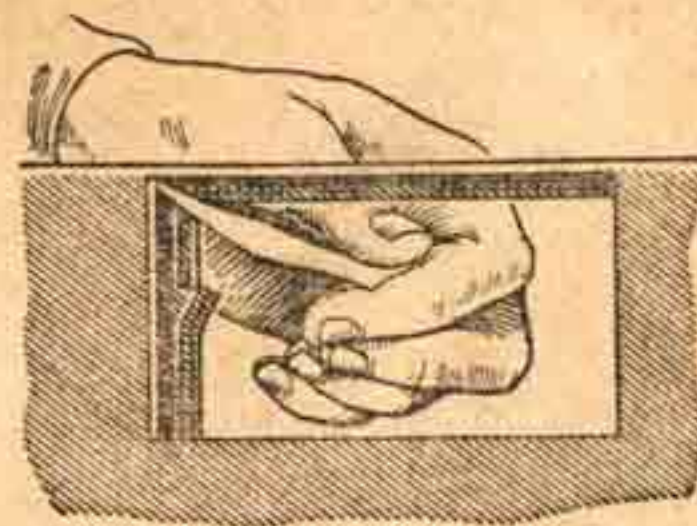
Проверка зазора между верхней площадкой боевой личинки и крышкой короба.
